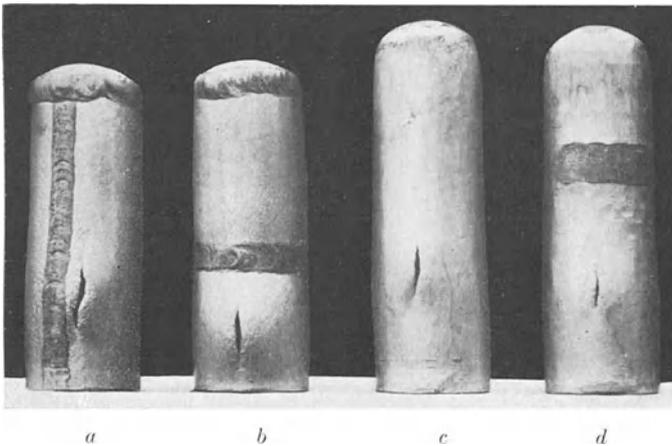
Geschweißte Versuchshohlkörper, durch Innendruck zerstört.
